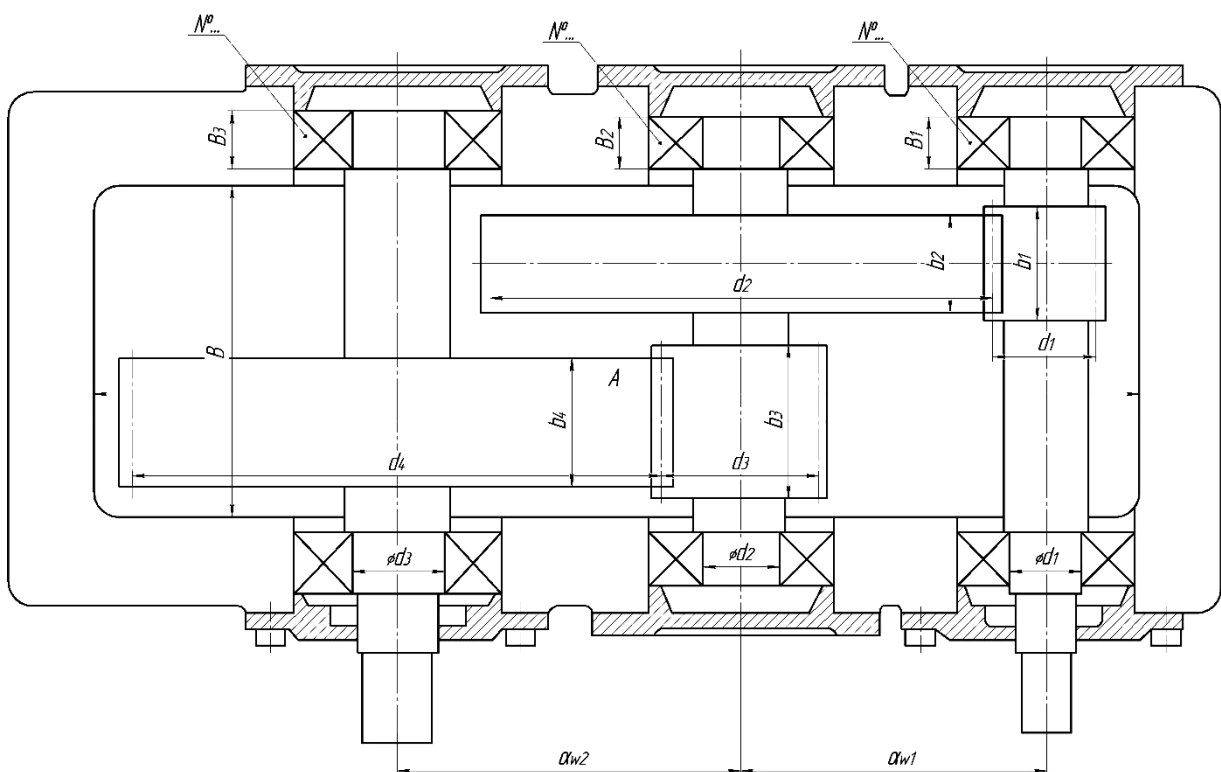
Циліндричний двоступеневий косозубий редуктор
